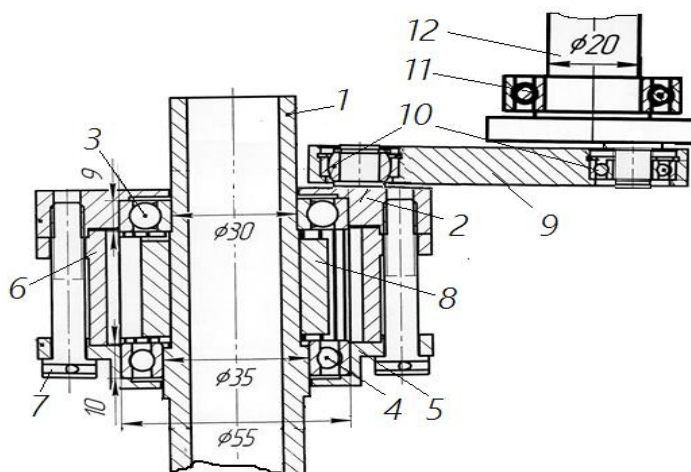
К сборке поворотного механизма перфоратора
